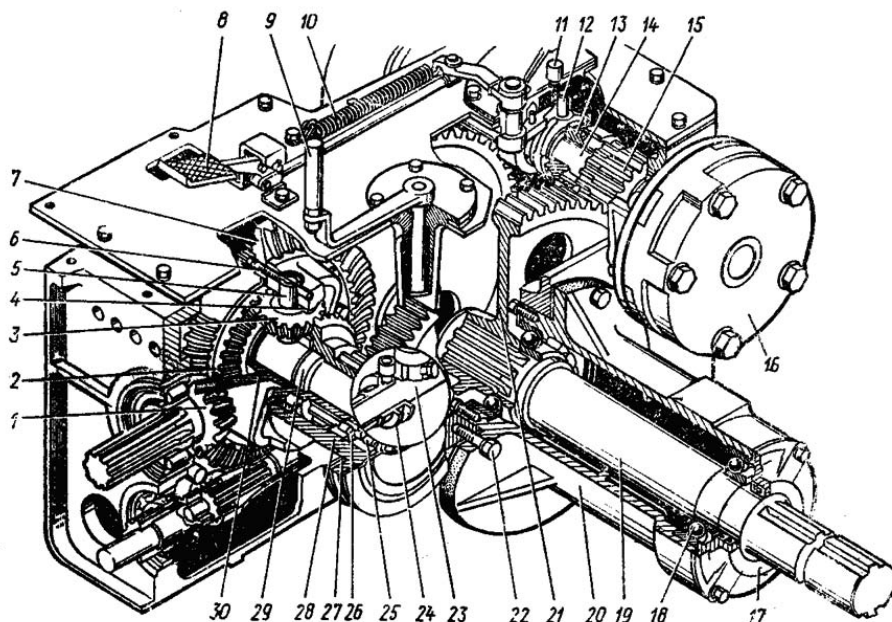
Задний мост. 1 — ведущая шестерня; 2 — полуосевая шестерня; 3 — сателлит; 4 — опорная шайба; 5 — ось сателлита; 6, 22 — болты; 8, 21 — ведомые шестерни; 18 — педаль механизма блокировки дифференциала; 9 — рычаг включения ВОМ; 10 — пружина; 11 — сапун; 12 — вилка; 13 — соединительная муфта; 14 — валик; 15 — тормозная шестерня; 16 — тормоз; 17 — крышка; 18, 25 — шарикоподшипники; 19 — полуось; 20 — рукав полуоси; 23 — вал отбора мощности; 24 — муфта включения ВОМ; 26 — роликоподшипник; 27 — регулировочные прокладки; 28 — стакан; 29 — вал главной передачи; 30 — ступица
